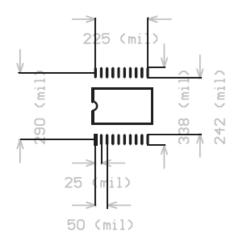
USB2I2C SSOP20 PCB 封装图 (MIL)
